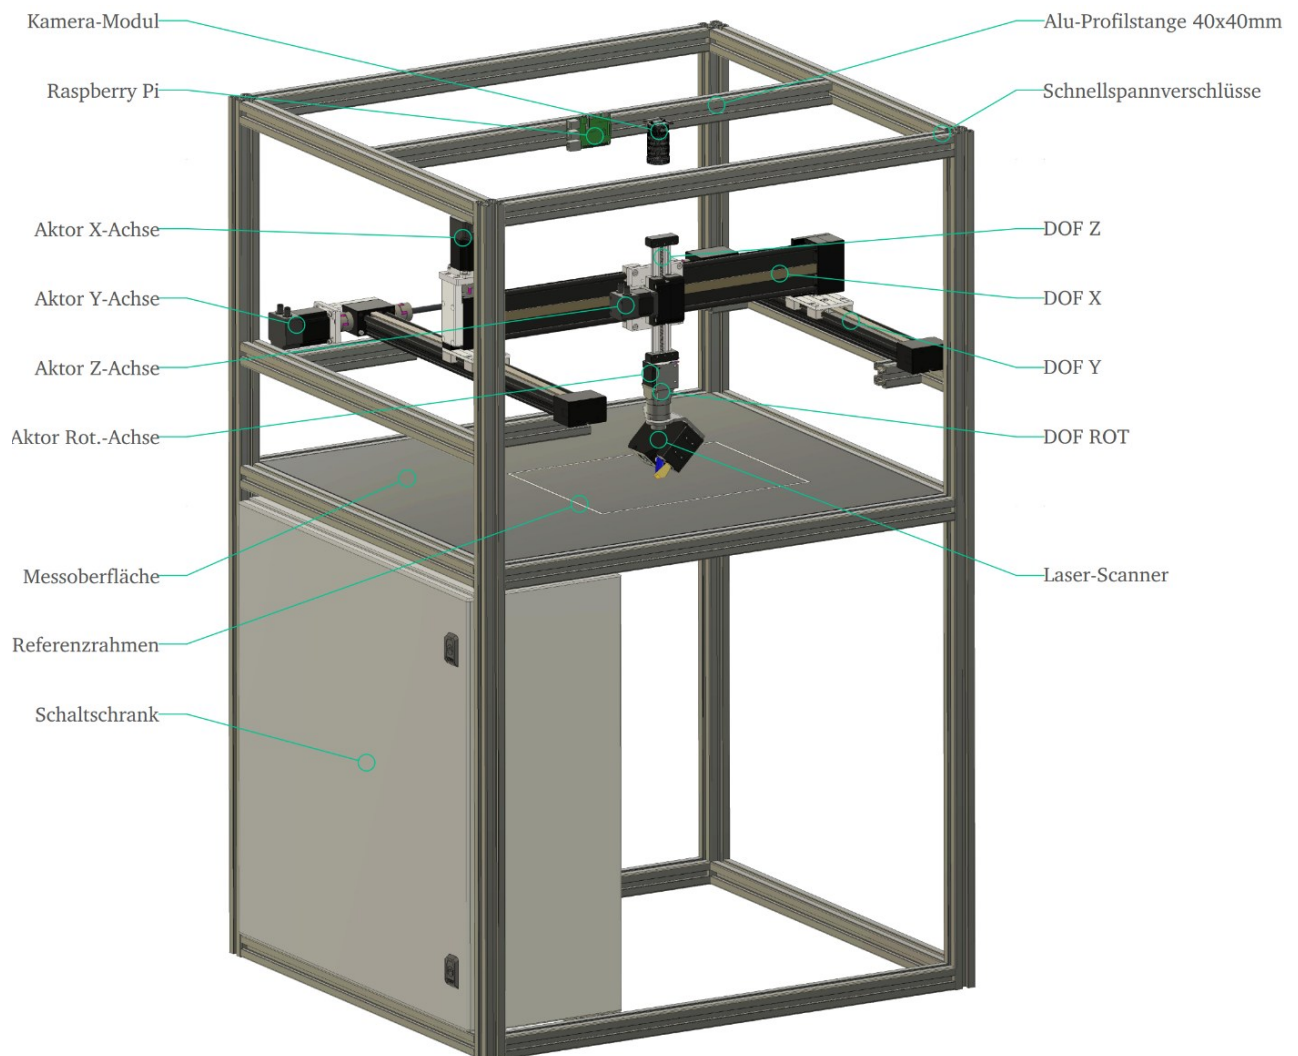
Gesamtansicht CAD-Prototyp mit ausgewiesenen Komponenten
